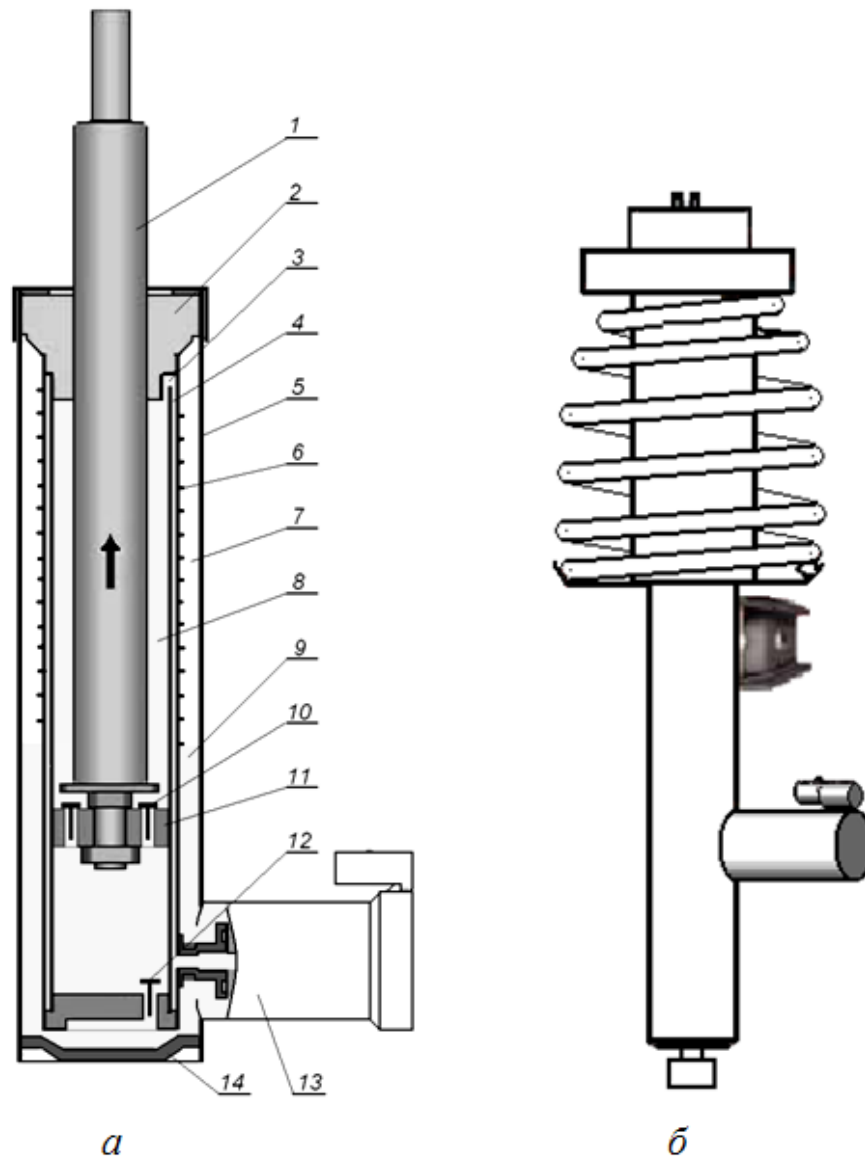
Будова керованого двотрубного газонаповненого амортизатора (*а*) і амортизаторної стійки (*б*): 1 – шток поршня; 2 – напрямна/ущільнення; 3 – пропускний отвір; 4 – кільцевий канал; 5 – трубка-резервуар; 6 – спіраль газосіння піни; 7 – газова подушка; 8 – робоча камера 1; 9 – робоча камера 2; 10 – поршневий клапан; 11 – поршень; 12 – клапан стиску; 13 – електромагнітний регульований клапан; 14 – дно
